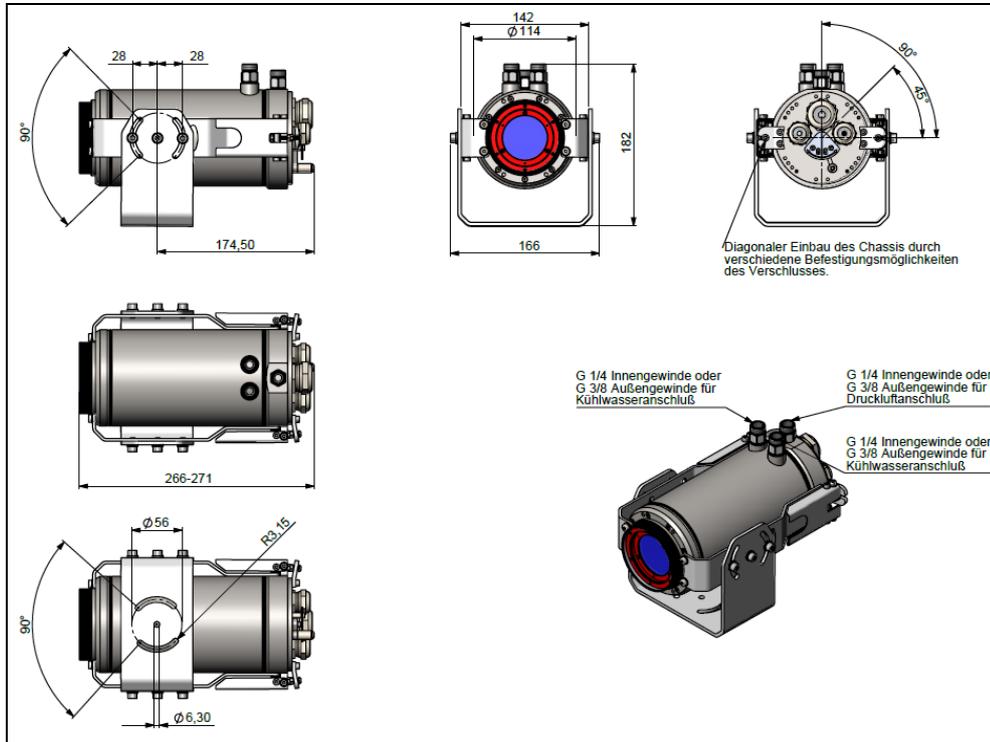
CoolingJacket Advanced, Standard-Version – Komplettansicht
